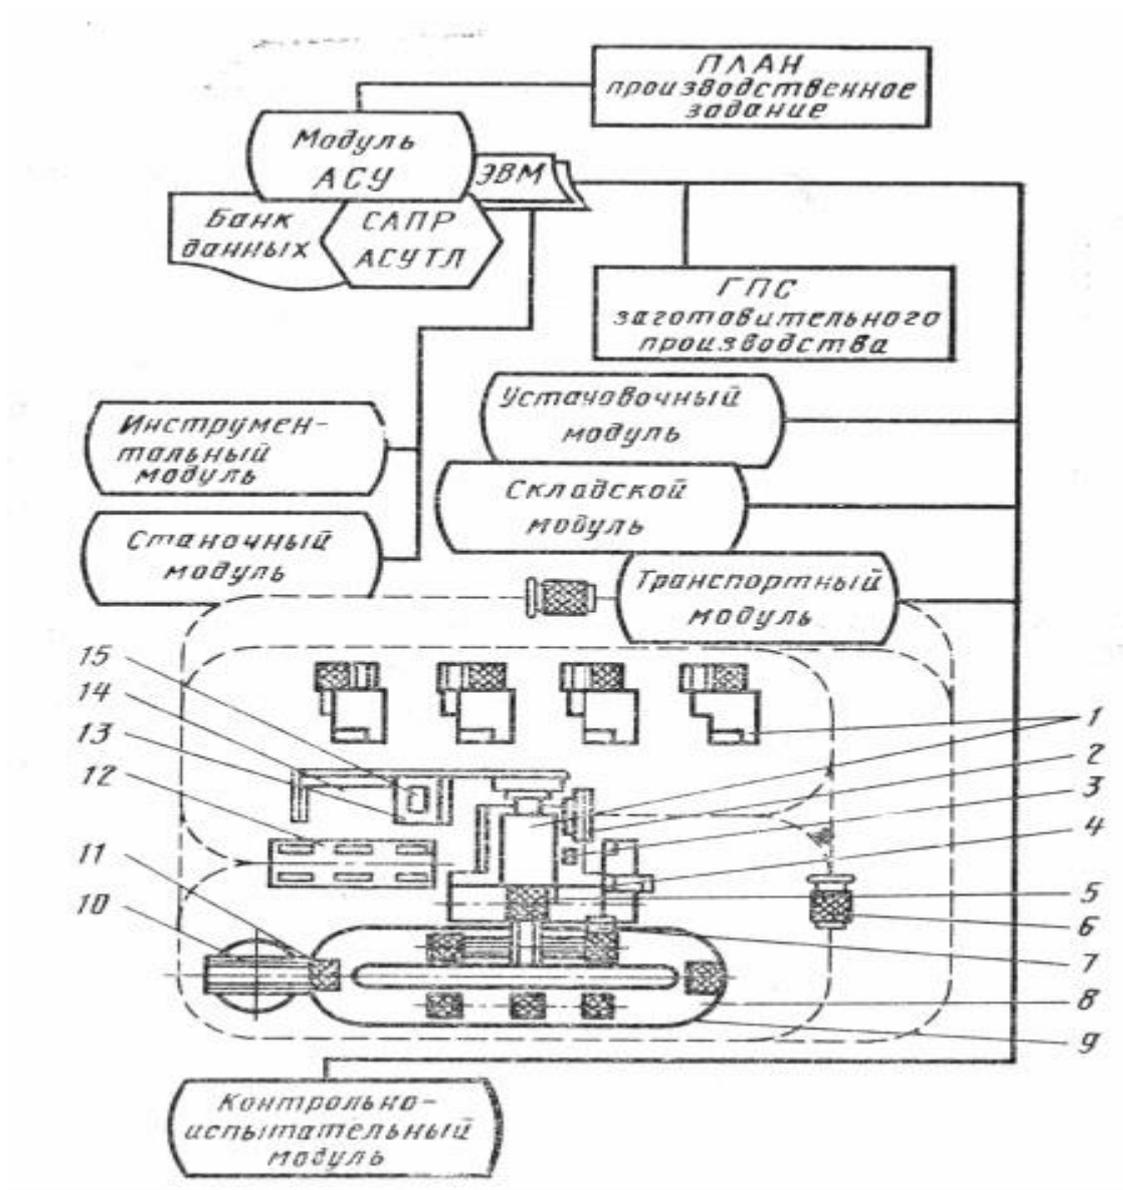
Структурная схема ГПС на базе многоцелевого станка типа обрабатывающий центр (ОЦ)
